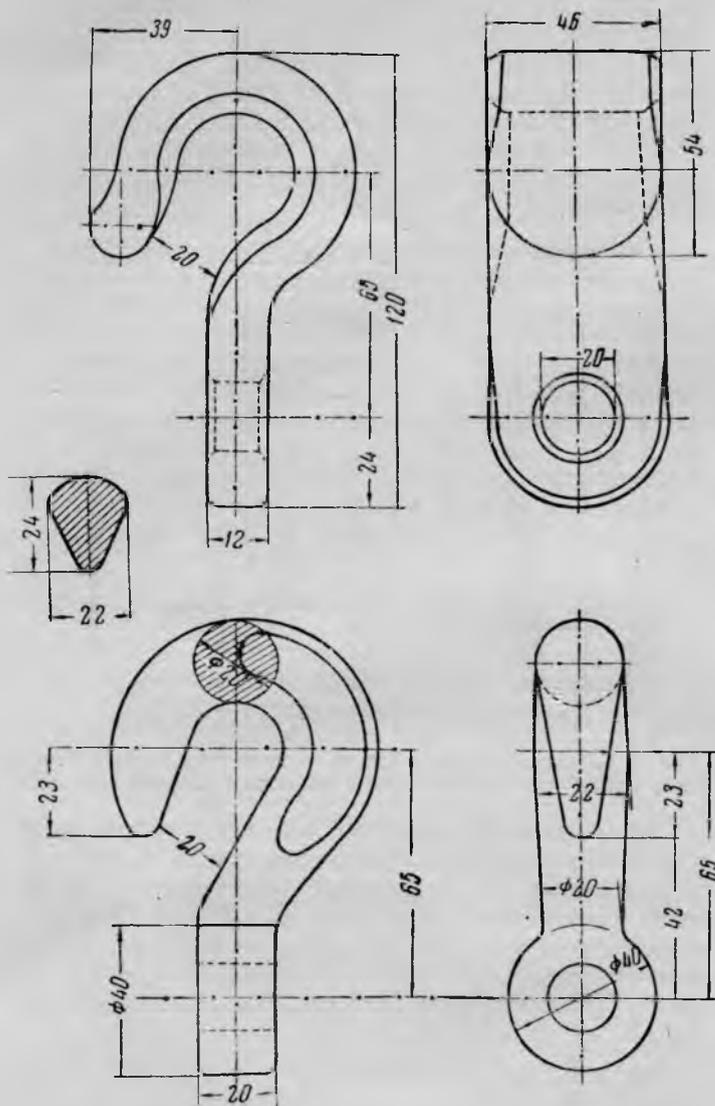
Чокерные крюки из полосовой (сверху) и круглой (снизу) стали
